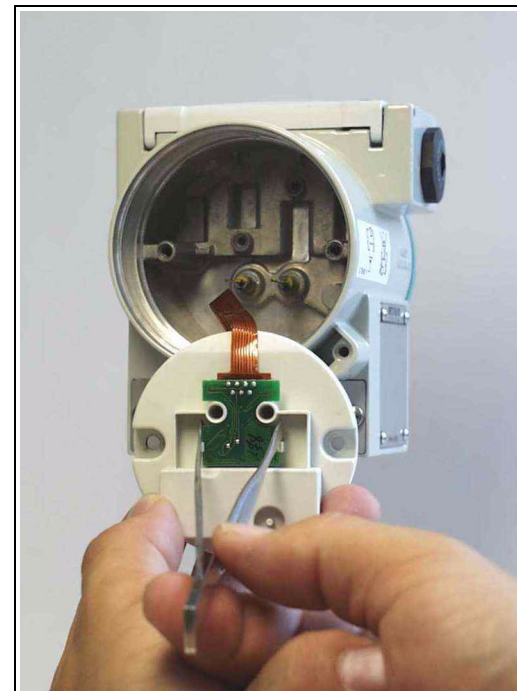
Abziehen der Messzellenplatine mit geeignetem Werkzeug, z.B: Pinzette bis Erzeugnisstand 29
